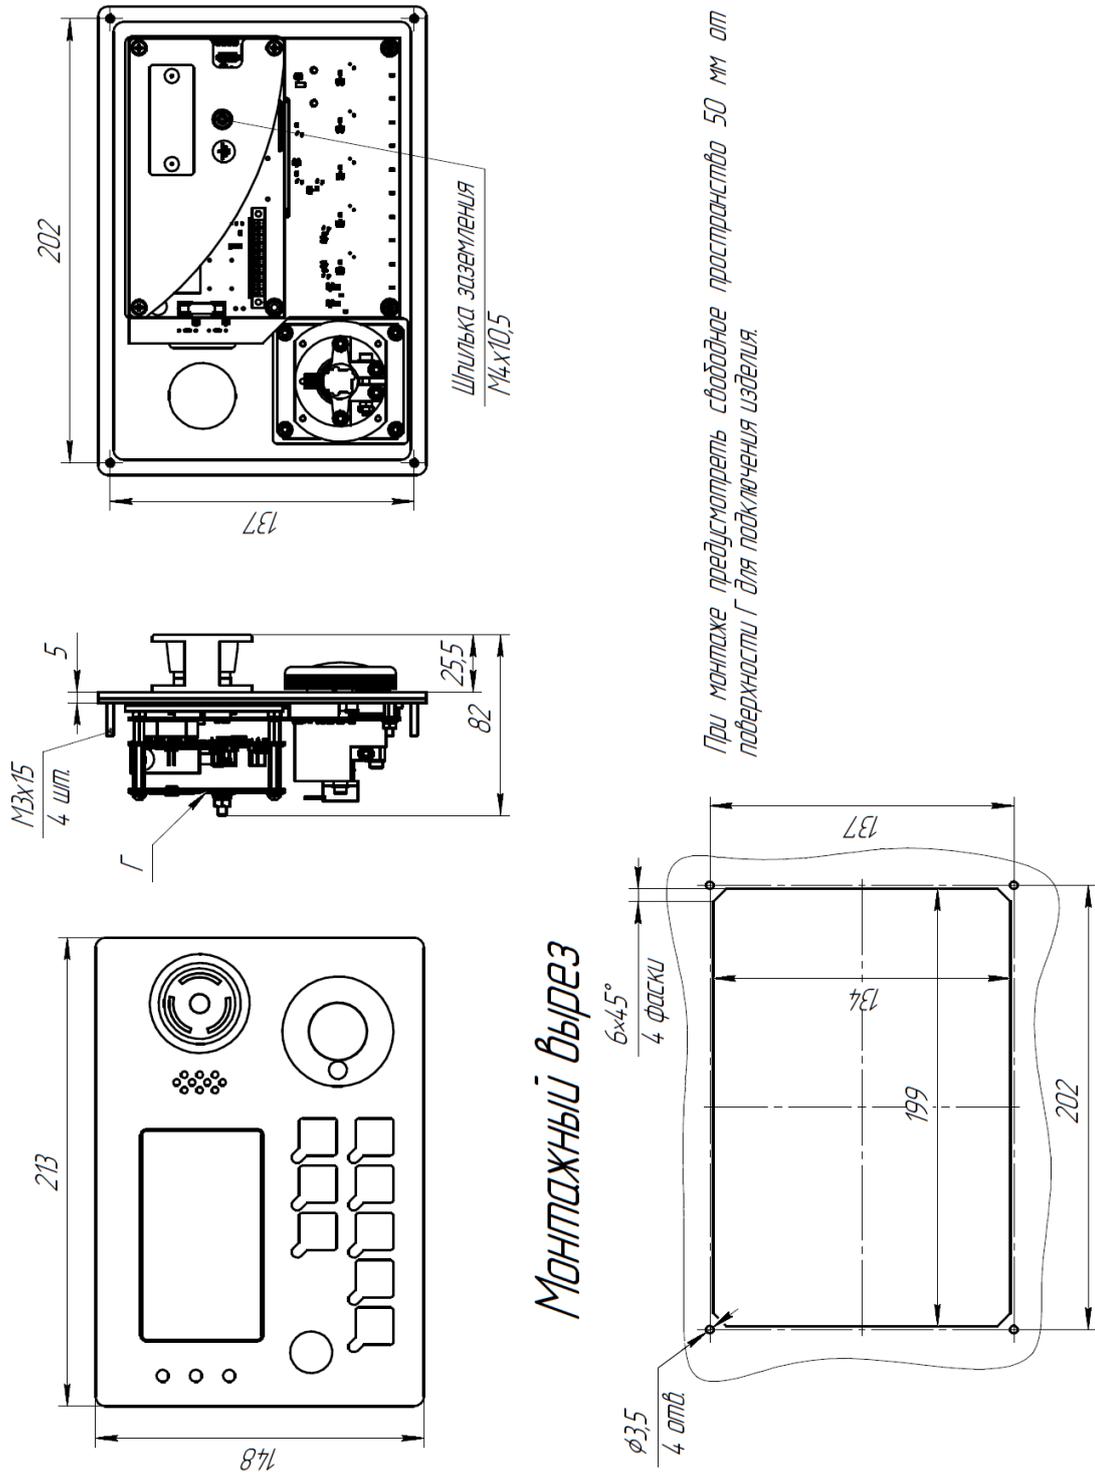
Габаритные и установочные размеры ПДУ-КМ (с ручкой)
